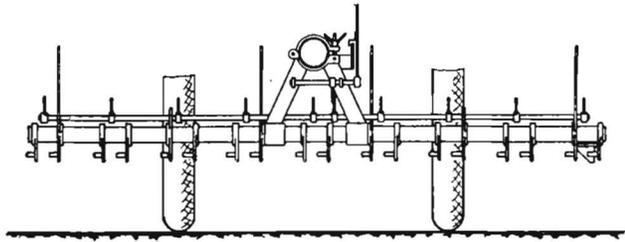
Getrenntes liegendes Werkzeugtragrohr und Aufzugsbock (mit 4 Spannschrauben)
